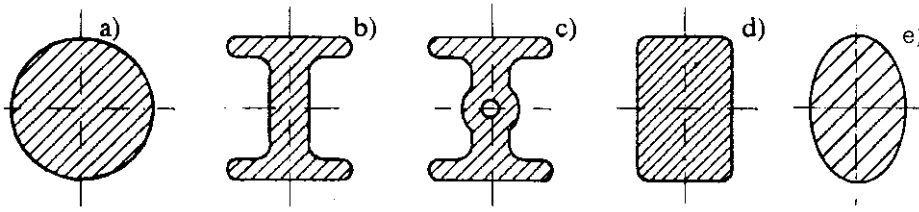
Kết cấu dầu nhỏ thanh truyền
